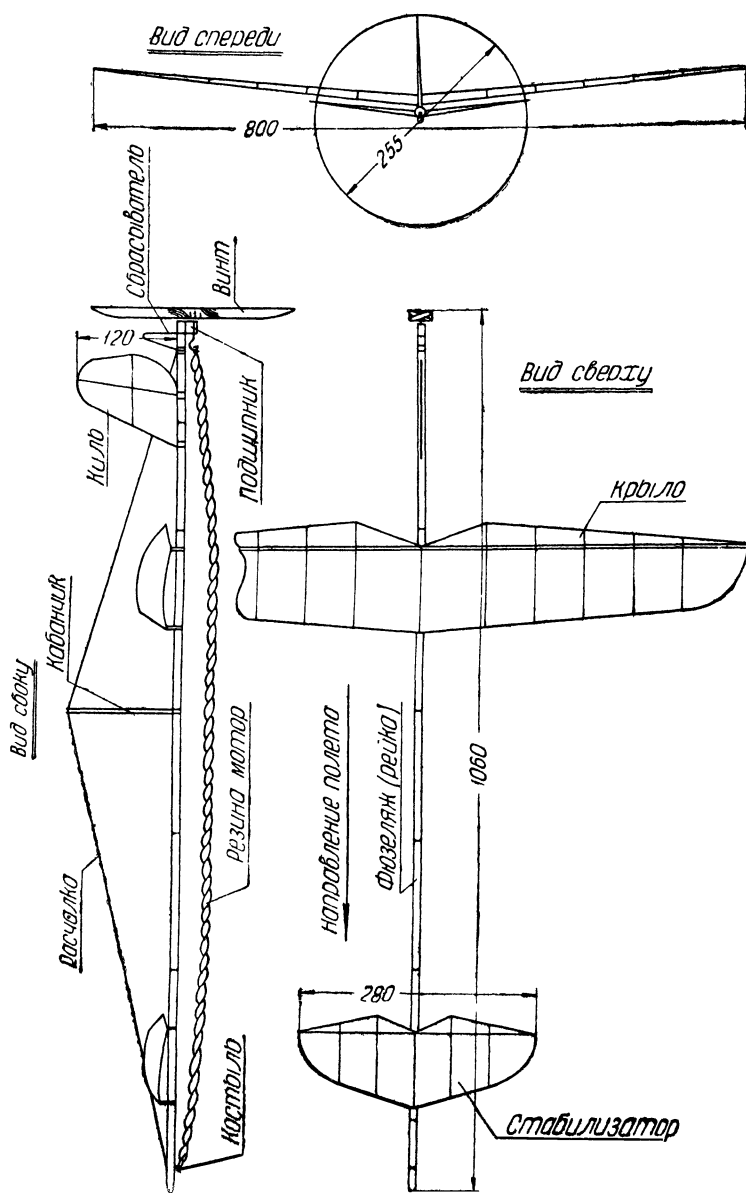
Схематический чертеж летающей модели самолета типа «утка» конструкции Гени Макарова
